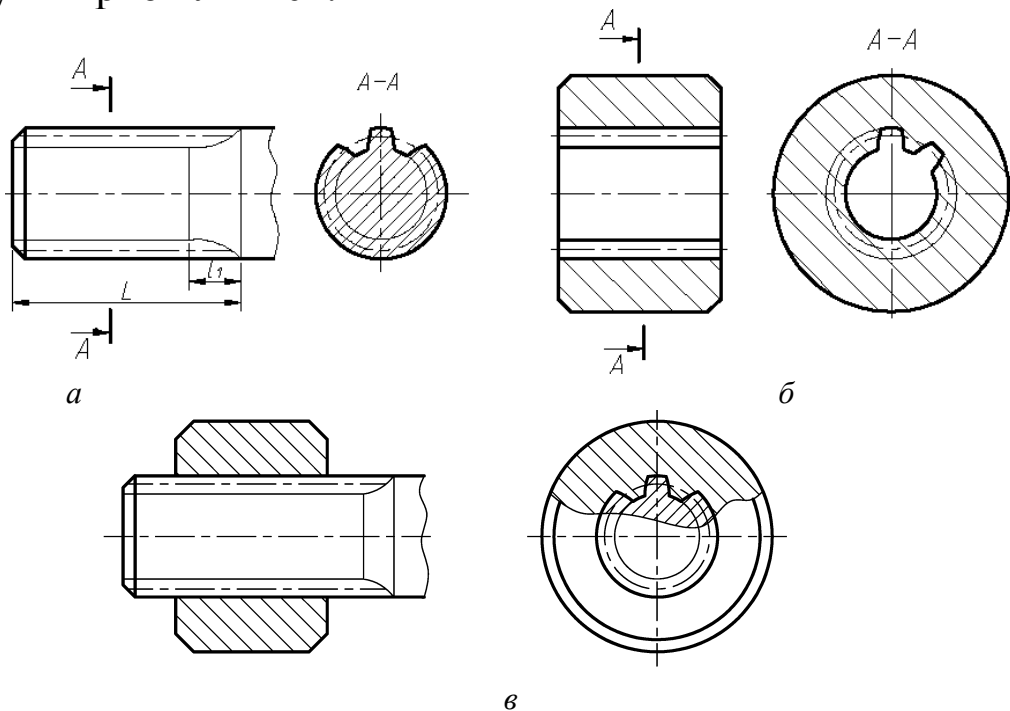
Изображение шлицевых деталей с эвольвентным профилем зуба:
